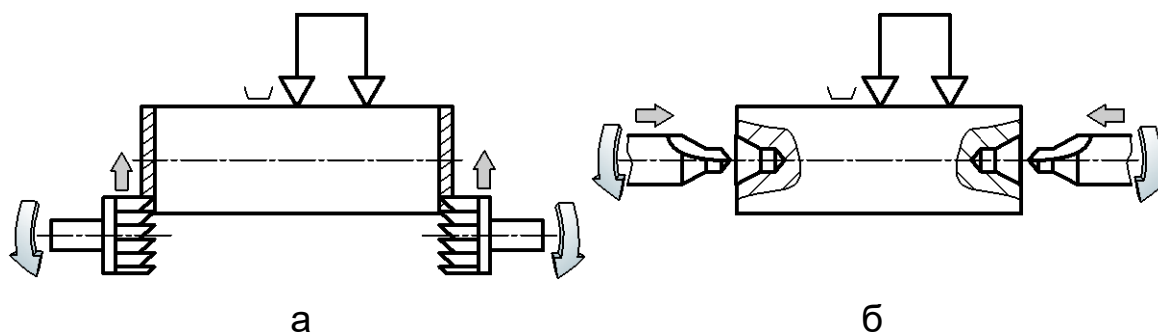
Схема работы фрезерно-центровального станка
